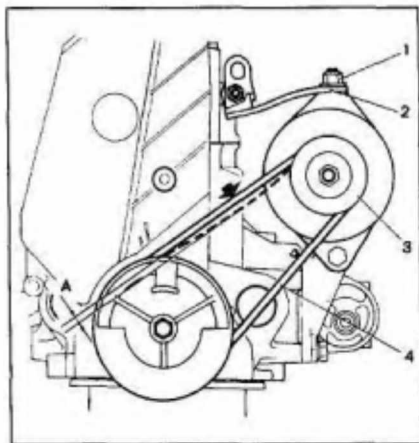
Регулировка натяжения ремня привода генератора: 1 — гайка; 2 — натяжная планка; 3 — генератор; 4 — ремень; А — прогиб ремня
